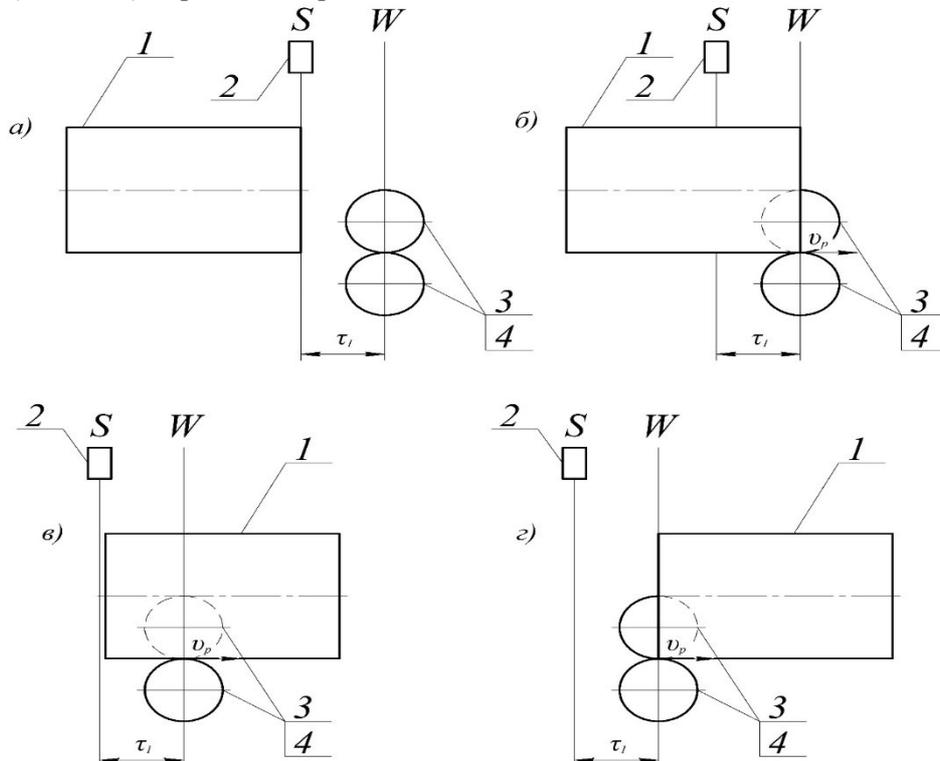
Схема прохождения заготовки барабана через зону сварки
